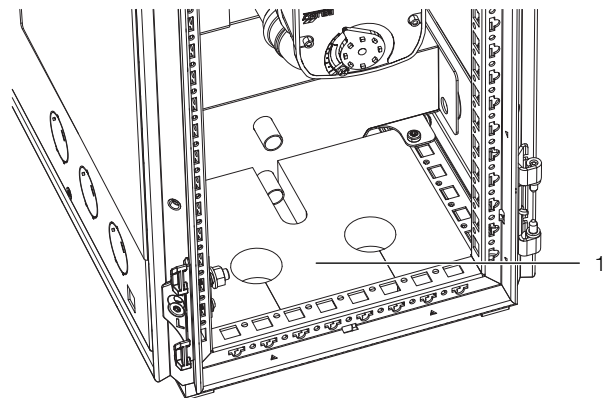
LCP CW Rückansicht – Raum zur Einführung der Anschlusschläuche
